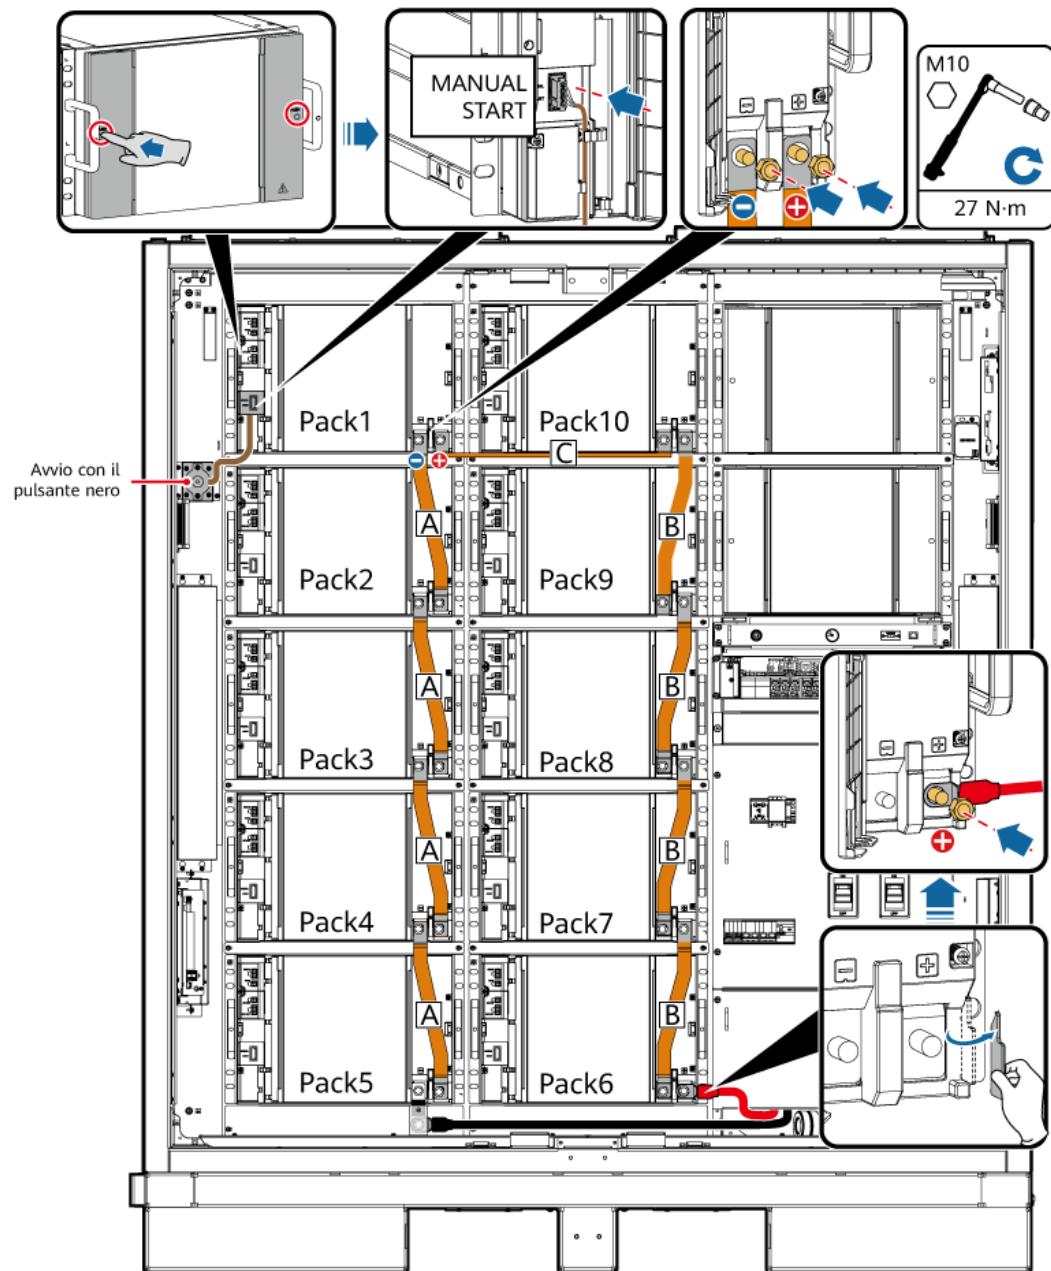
Installazione di cavi e barre di rame (modello 129 kWh)
